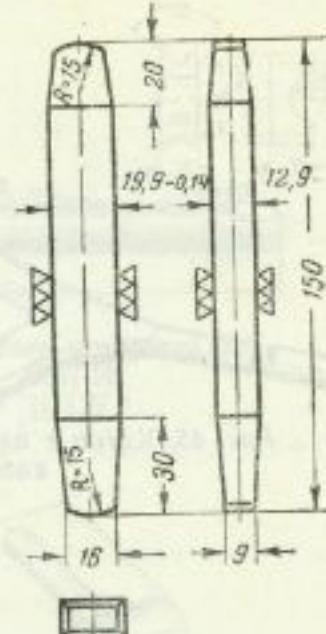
Оправка для коробки стопоров станка Д-ПП ПМ-26. Ст. 6, ГОСТ 380-41.
